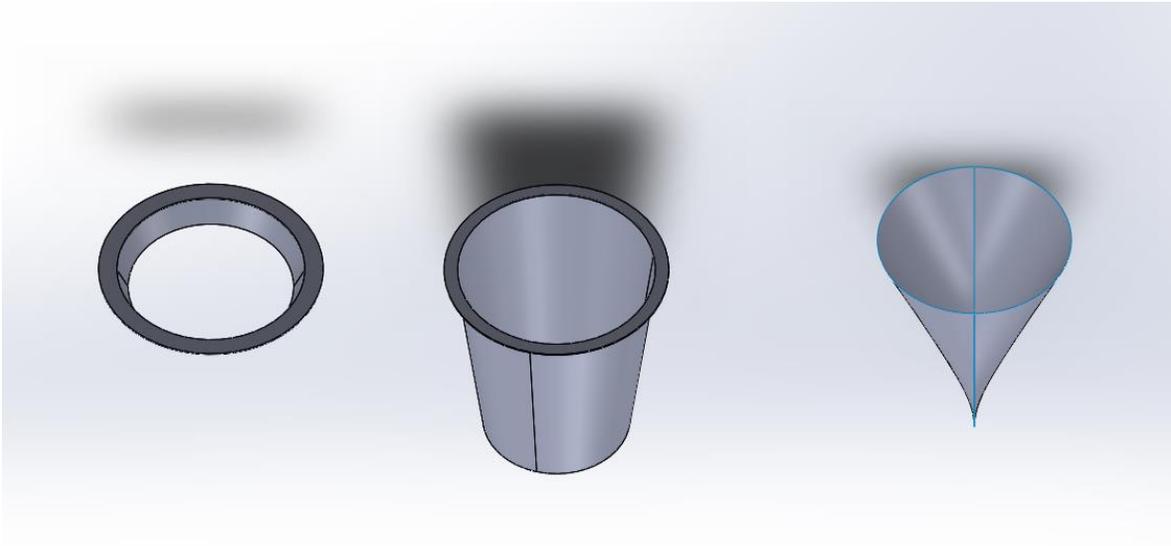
Vista en planta superior de los elementos de la cápsula de café (Diseño propio).
